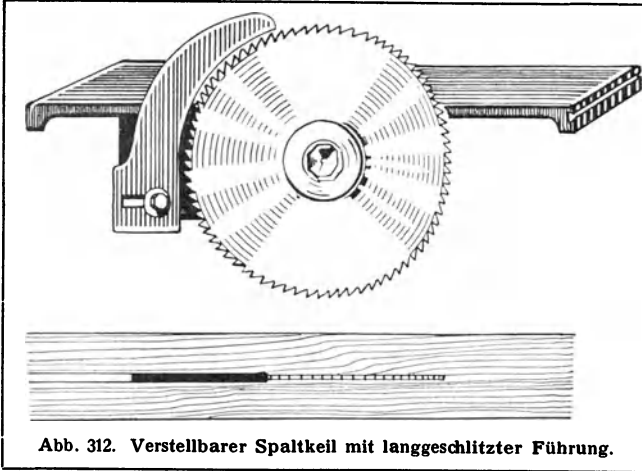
Verstellbarer Spaltkeil mit langgeschlitzter Führung.
